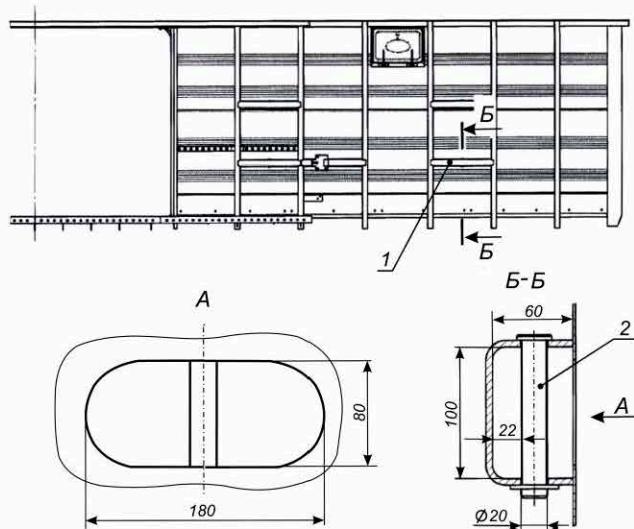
Устройства для закрепления грузов внутри вагона
